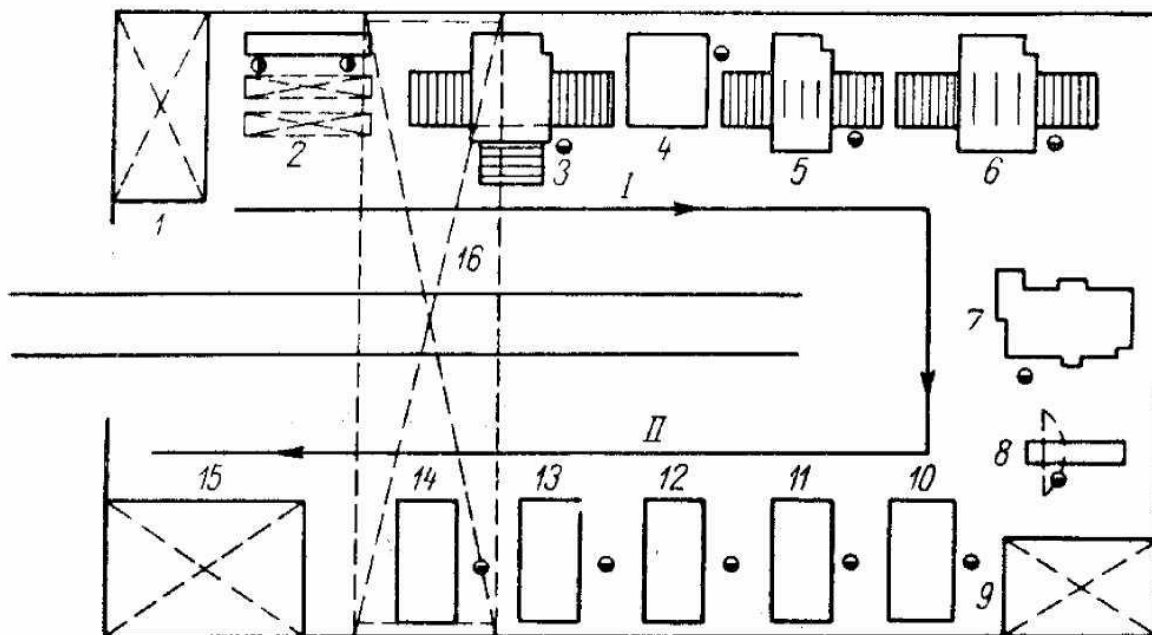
Схема размещения оборудования и рабочих мест заготовительного и сборочно-сварочного участков по изготовлению сварной конструкции
